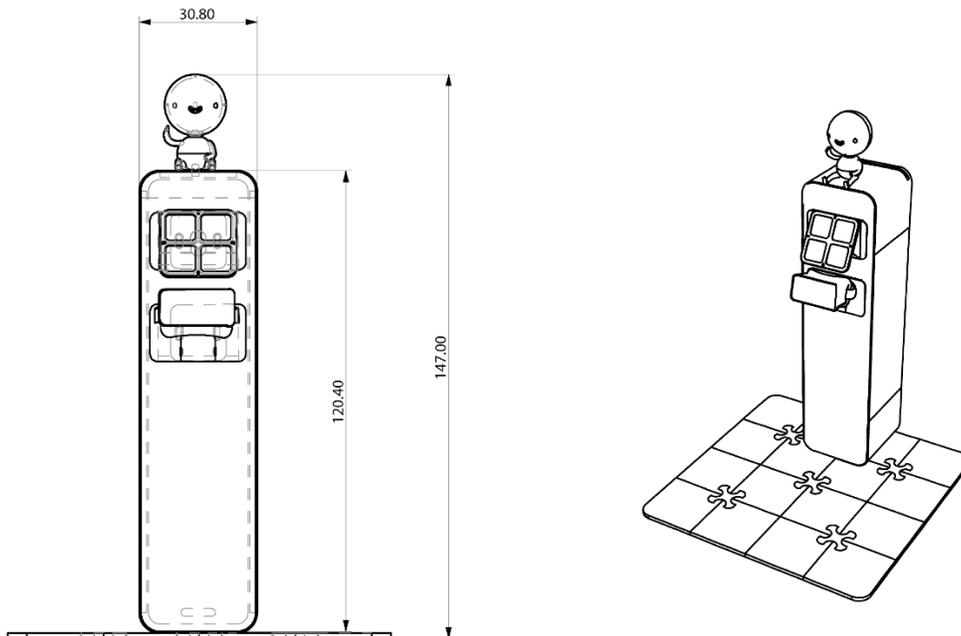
Plano General. Vista Frontal. 2018. Elaboración Propia
